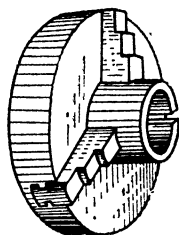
Применение разрезной втулки для точной установки заготовки.
